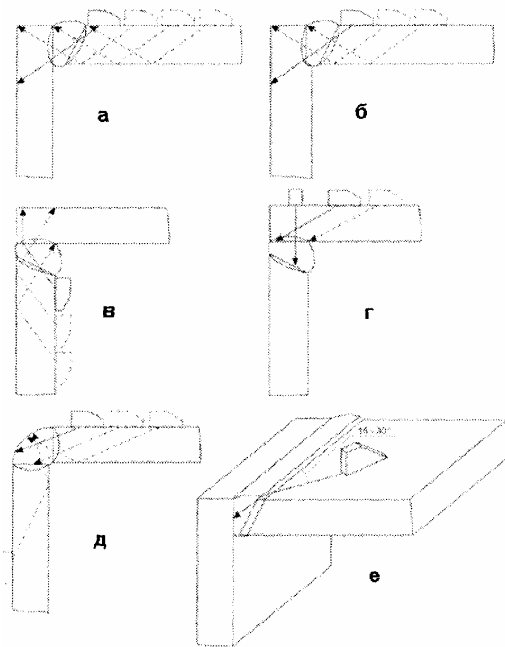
Схемы контроля угловых сварных соединений
